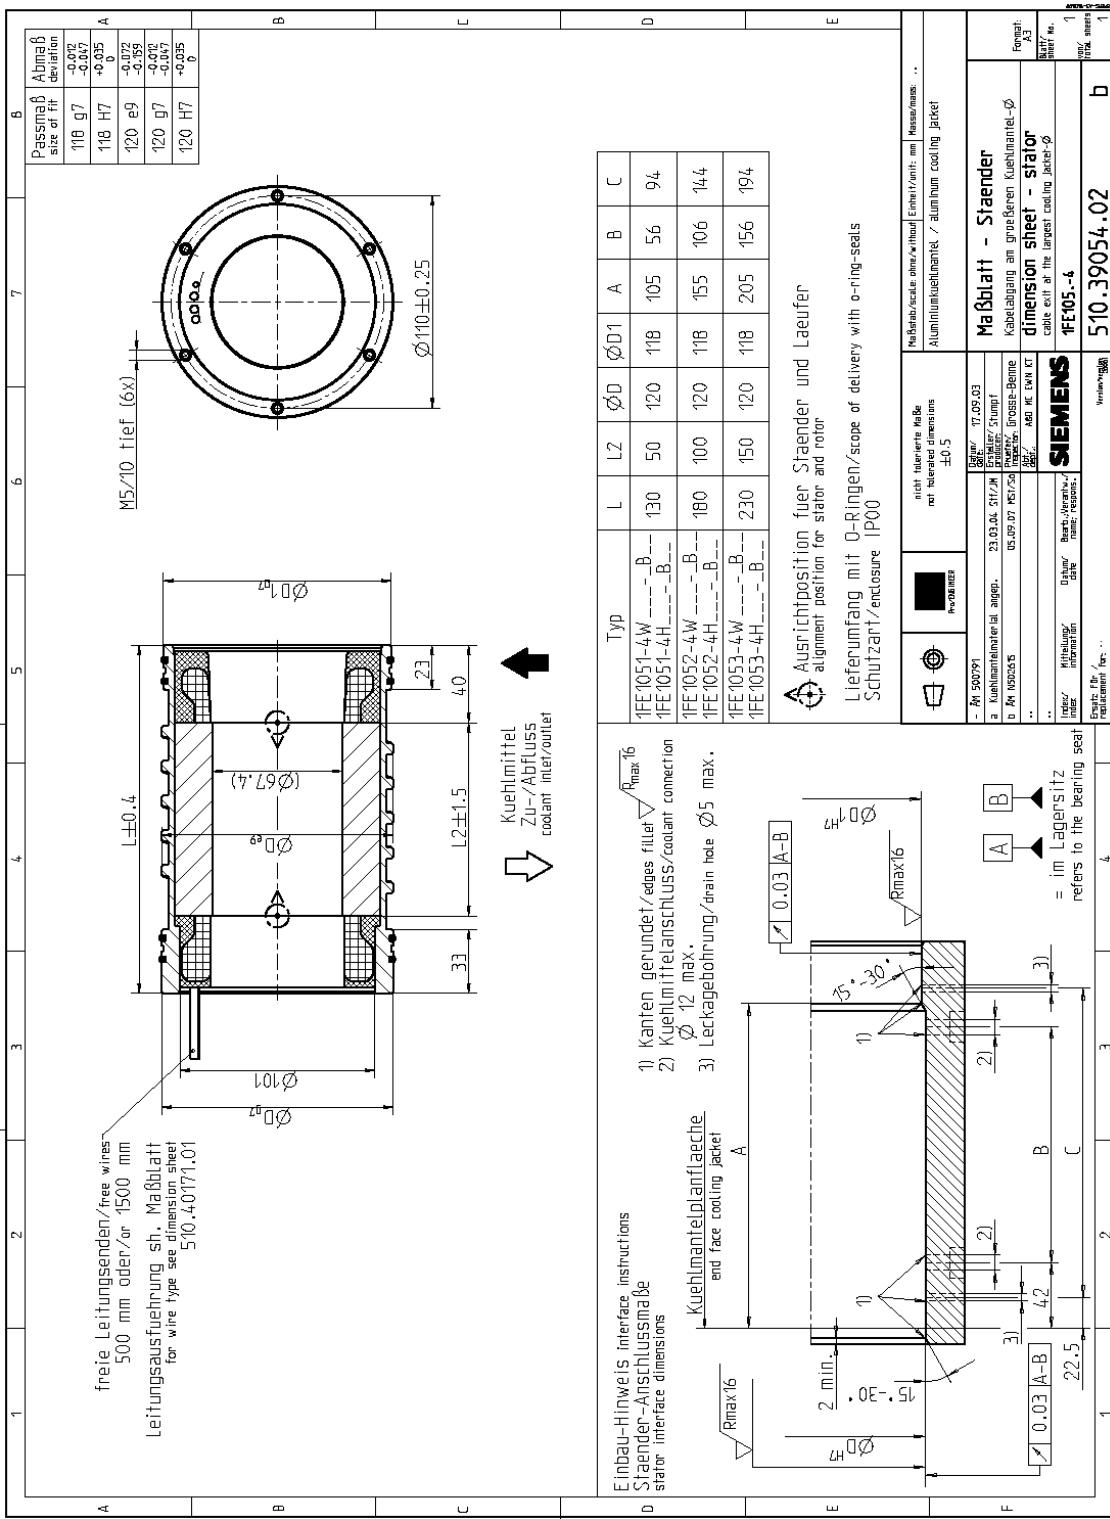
1FE105□-4, Ständer mit Kühlmantel, Kabelabgang am größeren Kühlmanteldurchmesser
